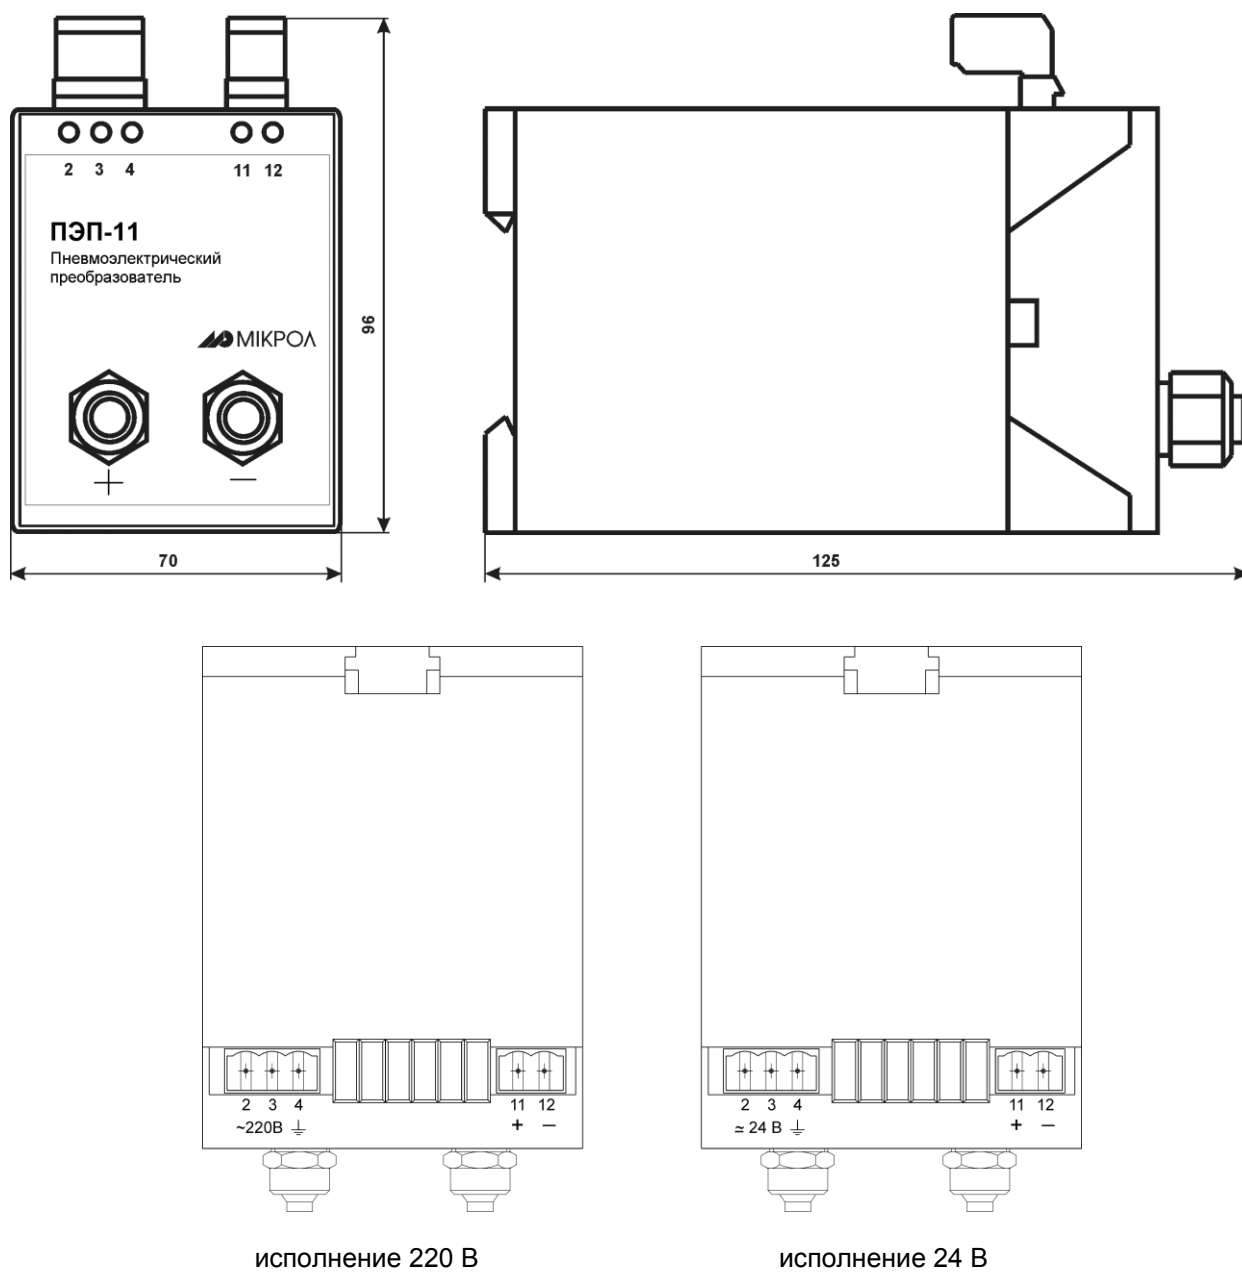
Внешний вид и габаритные размеры ПЭП-11(преобразователь разности давления)
